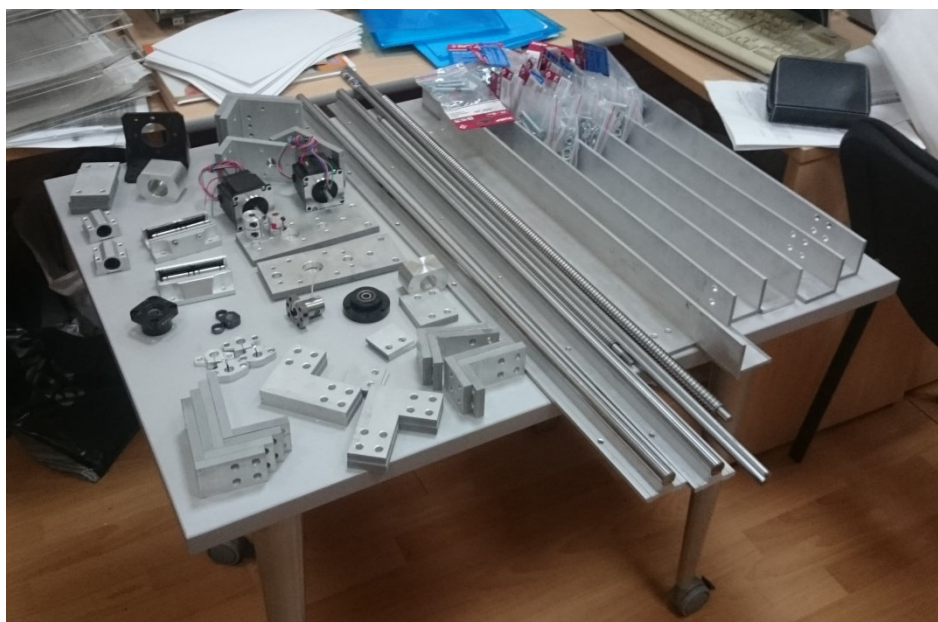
Стол для монтажа оборудования и детали, закупленные и изготовленные по оригинальным чертежам.
